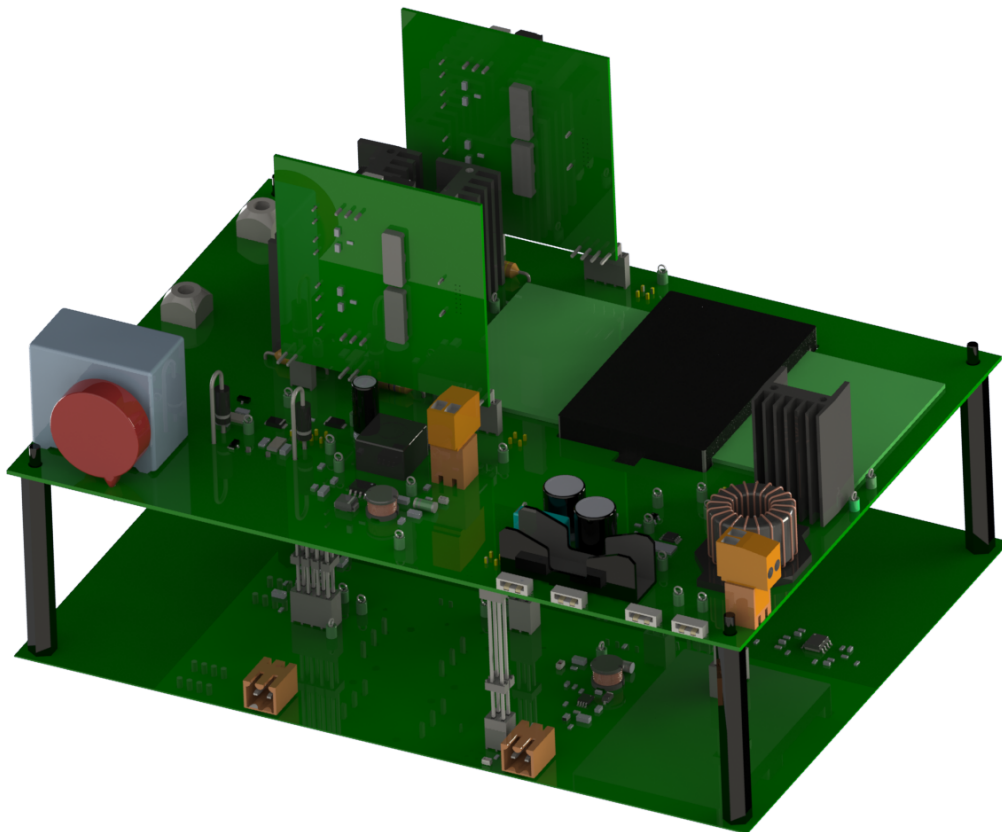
Dibuix 3D de la PCB *BlackHole*.
